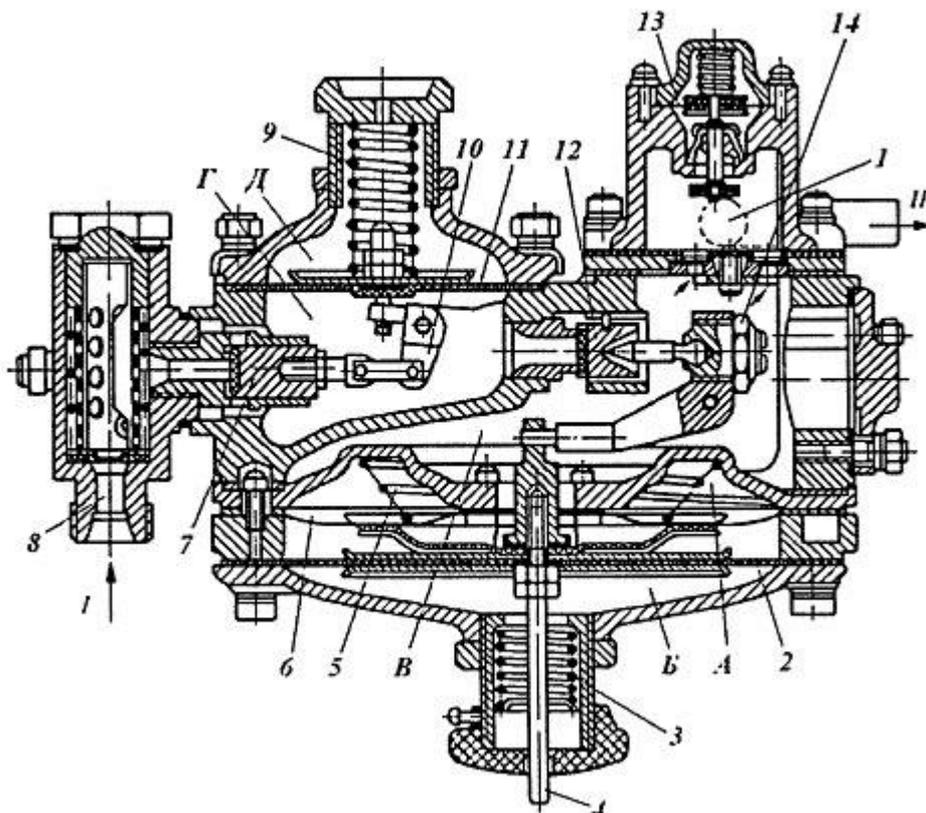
Двухступенчатый газовый редуктор низкого давления
